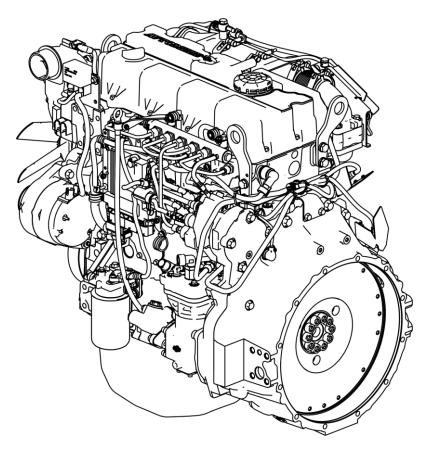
а – Двигатель ЯМЗ-53443-20 (общий вид слева)
